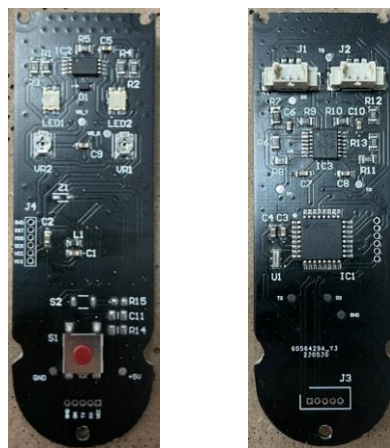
Resultado de la fabricación y montaje de la placa de adquisición
